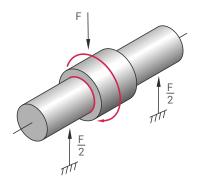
Umfangslast, rotierende Belastung, Welle steht, Buchse dreht sich.
